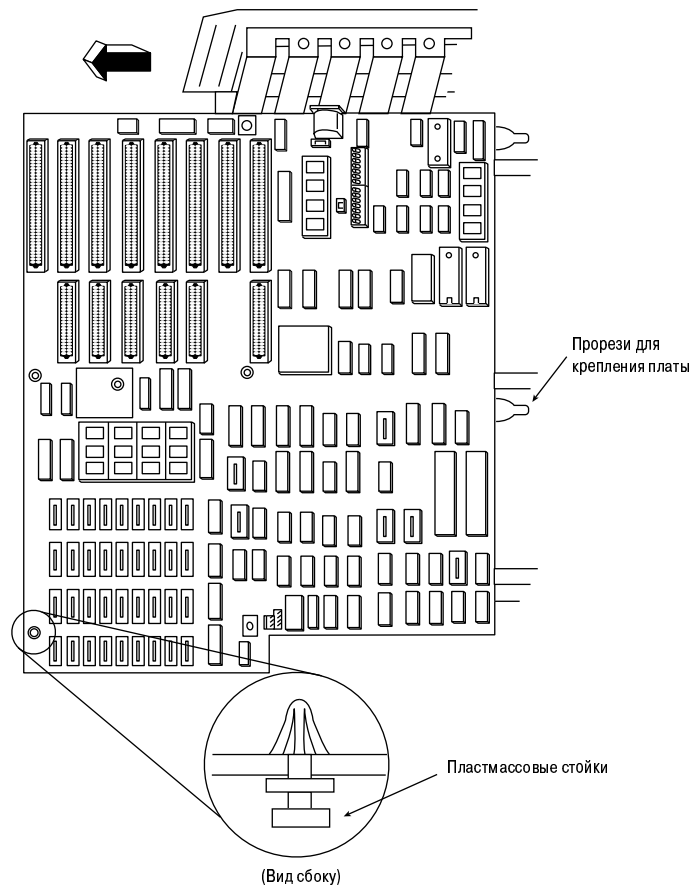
Установка пластмассовых стоек в новую системную плату
